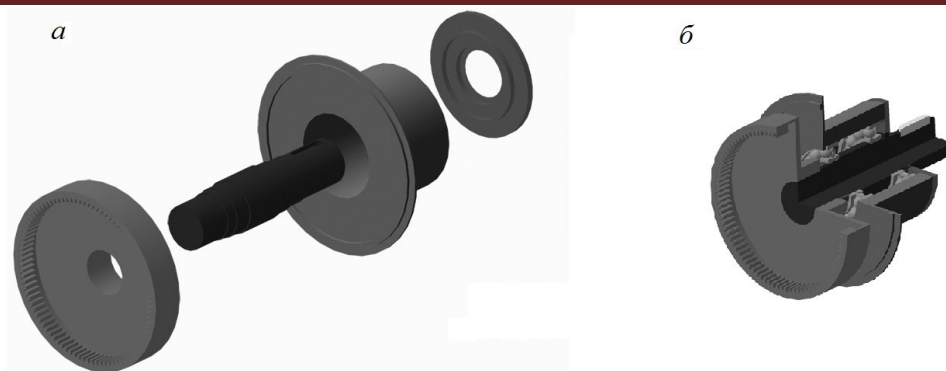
Комп'ютерні моделі деталей зубчастого колеса – епіцикла, введеного вала, елементів корпуса
